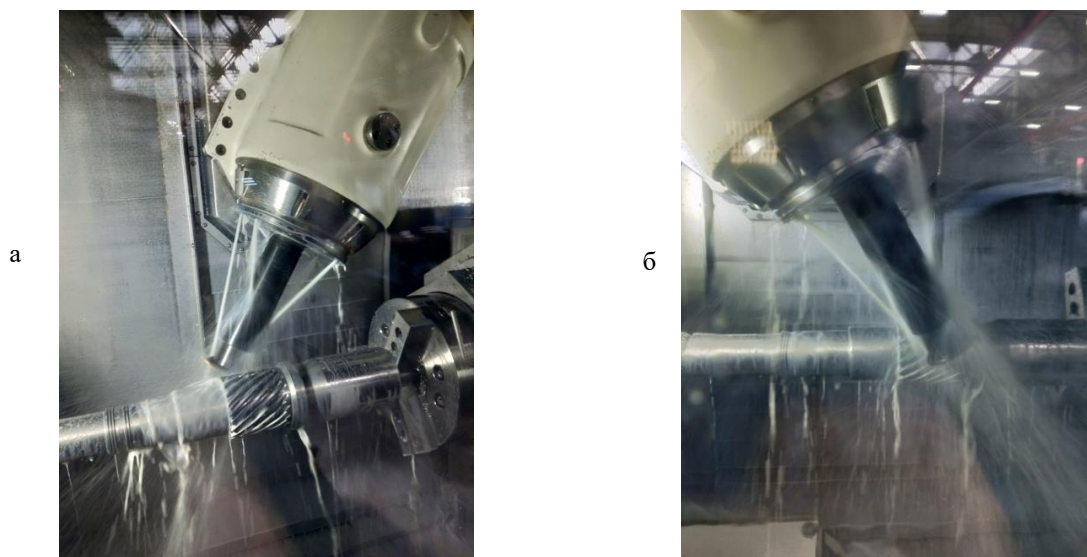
Чистовая обработка впадин зубчатого венца опытной детали дисковой фрезой Coromill 161 при поперечном перемещении: а – по левой стороне; б – по правой стороне впадины зубчатого колеса
